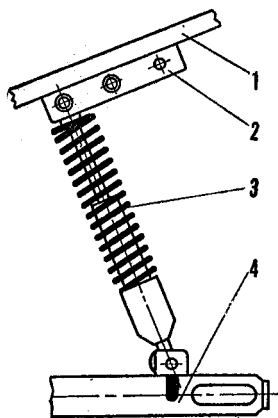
Установка косынки с отверстиями для изменения положения амортизатора: 1 — рама; 2 — косынка; 3 — амортизатор; 4 — перо задней вилки
